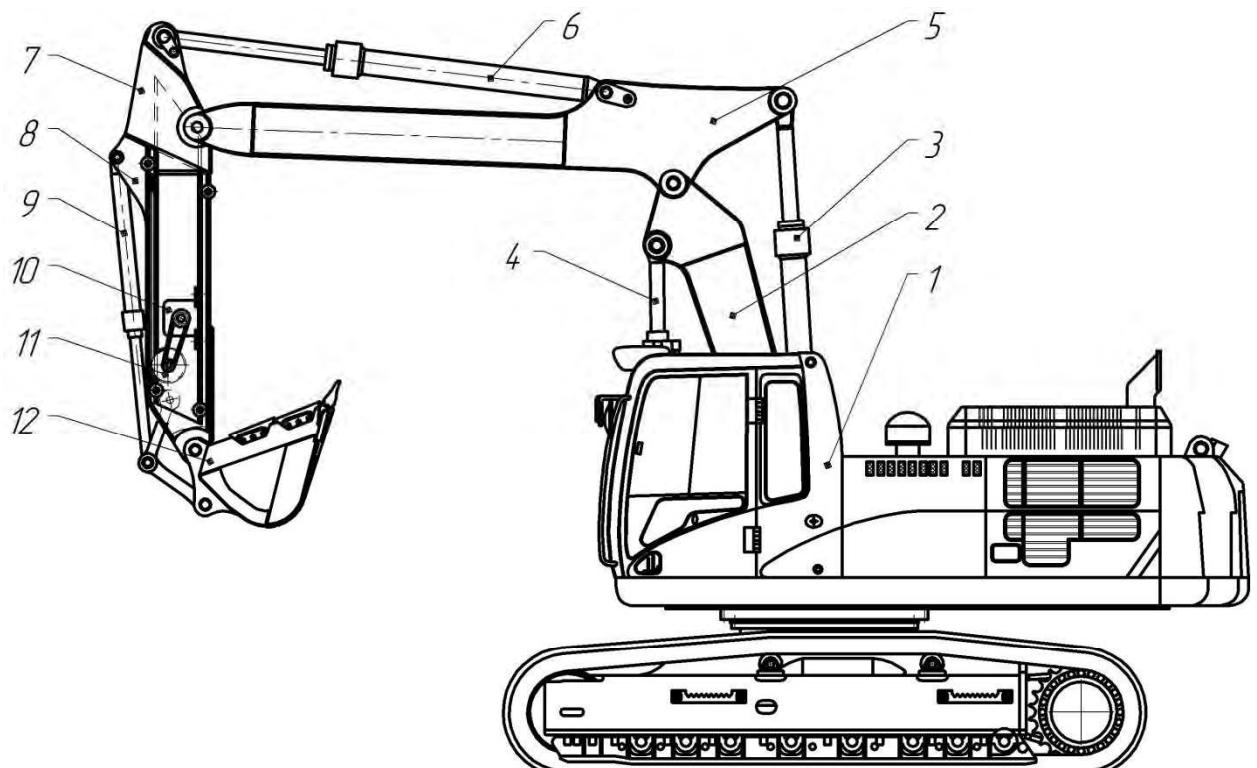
Загальний вигляд одноківшевого екскаватора з телескопічною рукояттю: 1 – базовий трактор; 2 – нижня частина стріли; 3, 4, 6, 9 – гідроцилінди; 5 – верхня частина стріли; 7 – рукоять; 8 – висувна секція рукояті; 10 – гідромотор; 11 – зубчасто-рейковий механізм; 12 - ківш.
